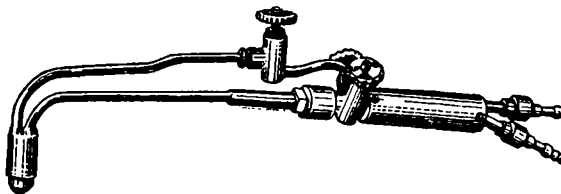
Ацетиленокислородный резак для ручной газовой резки
